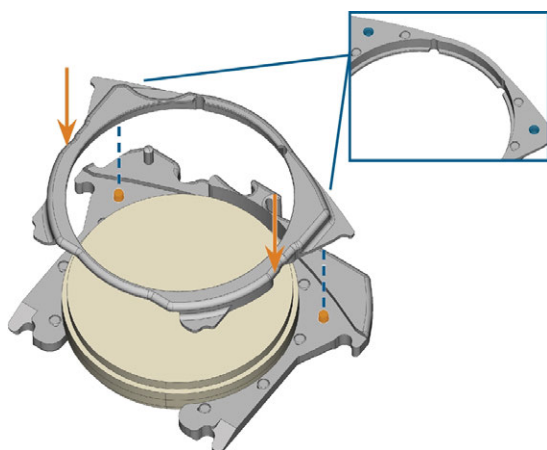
PLACEMENT DU COUVERCLE DU CADRE DE PIÈCES BRUTES (GOUPILLES DE POSITIONNEMENT MARQUÉES EN ORANGE, ENCOCHES MARQUÉES EN BLEU)
